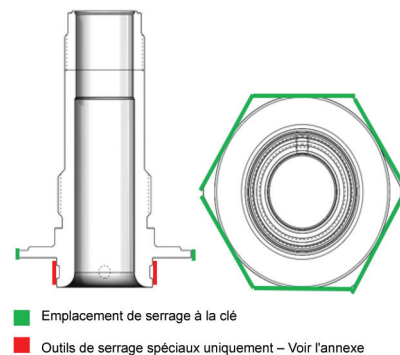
Emplacements de serrage de la buse de détection intégrée
